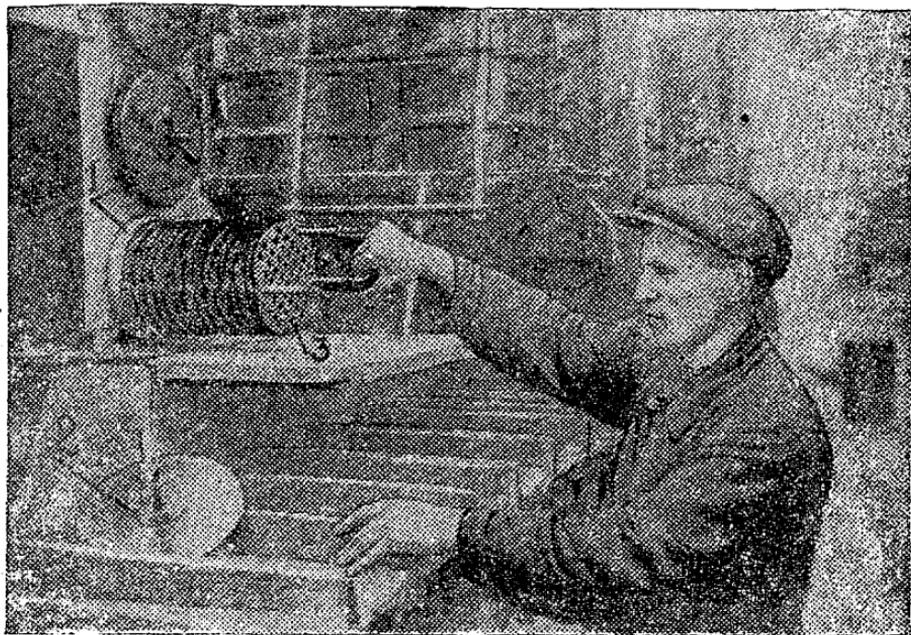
Разборка пластинчатого очистителя: 1—цилиндр пластинчатого очистителя; 2—крышки цилиндров; 3—секция.
